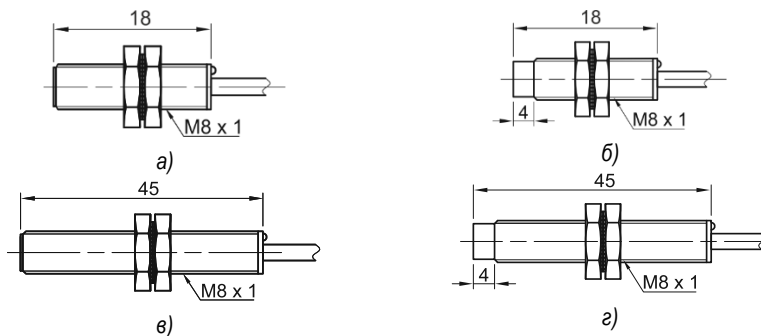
Габаритные и установочные размеры датчиков LA08
